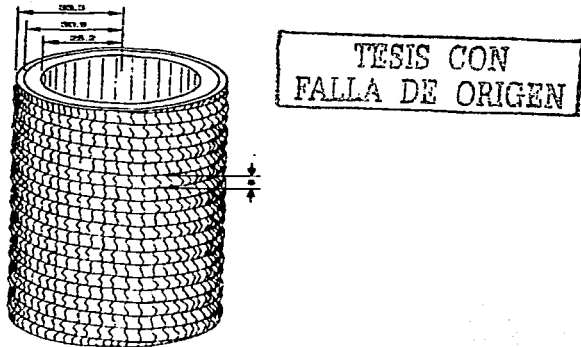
Esquema de una muestra de tubo con soldadura [67].
